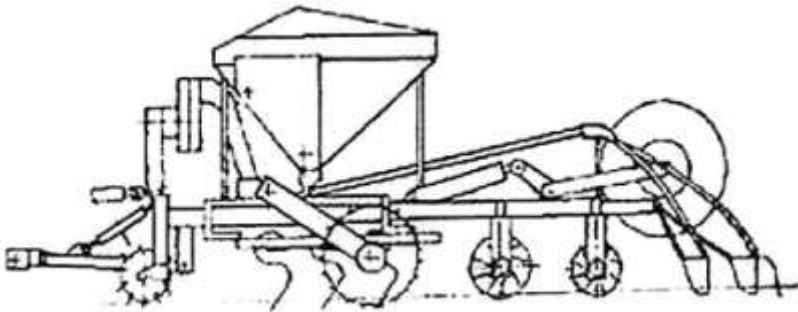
Комбинированный почвообрабатывающе-посевной агрегат АПП-3,0 (АПП-4,5; АПП-6)
